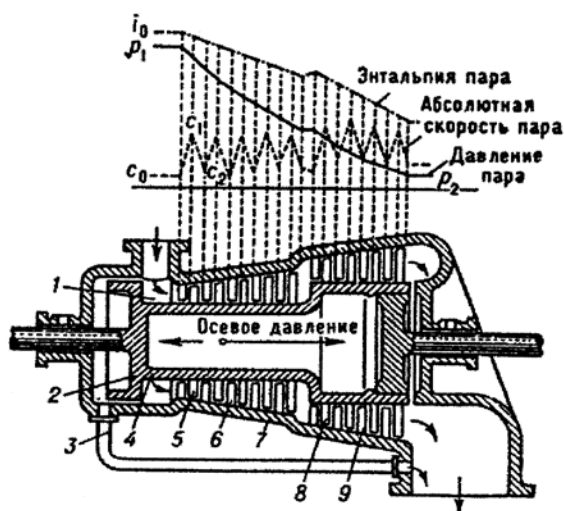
Схематический разрез небольшой реактивной турбины: 1 – кольцевая камера свежего пара; 2 – разгрузочный поршень; 3 – соединительный паропровод; 4 – барабан ротора; 5, 8 – рабочие лопатки; 6, 9 – направляющие лопатки; 7 – корпус.
